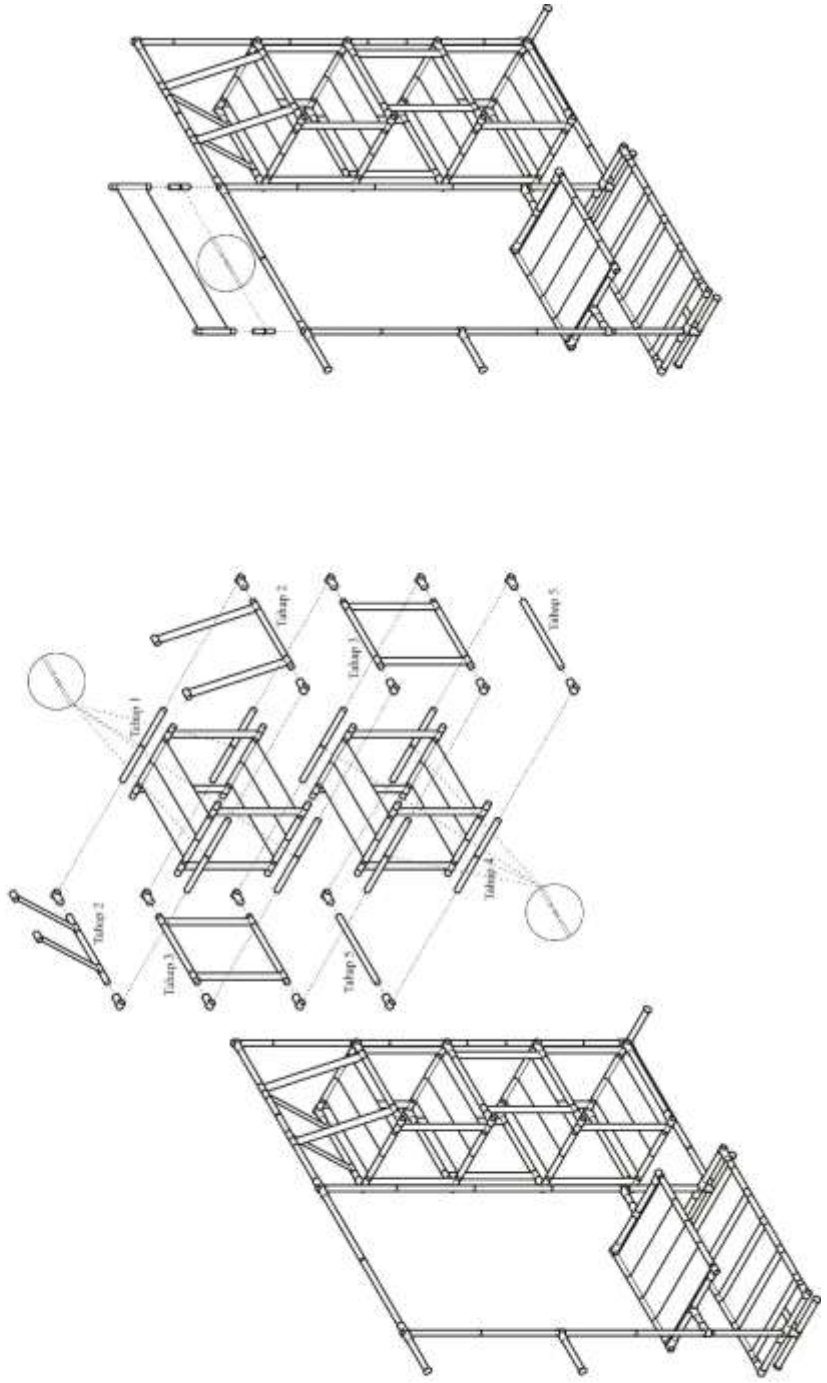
Detail Pipa, Kain dan Sambungan Modul 3
